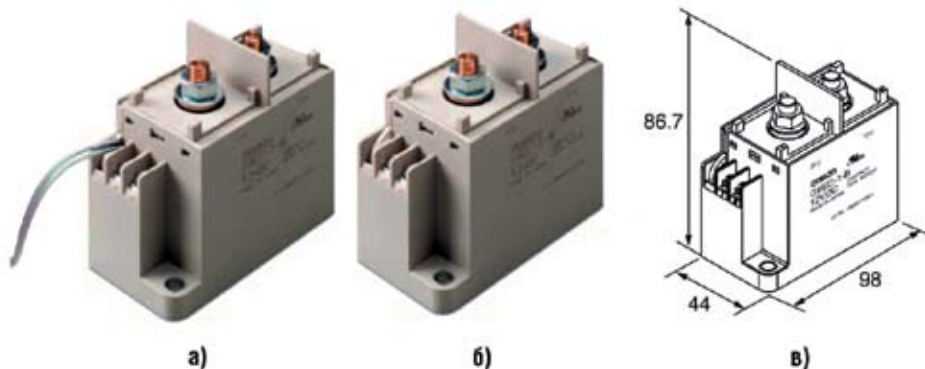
Внешний вид и габаритные размеры реле G9EC
